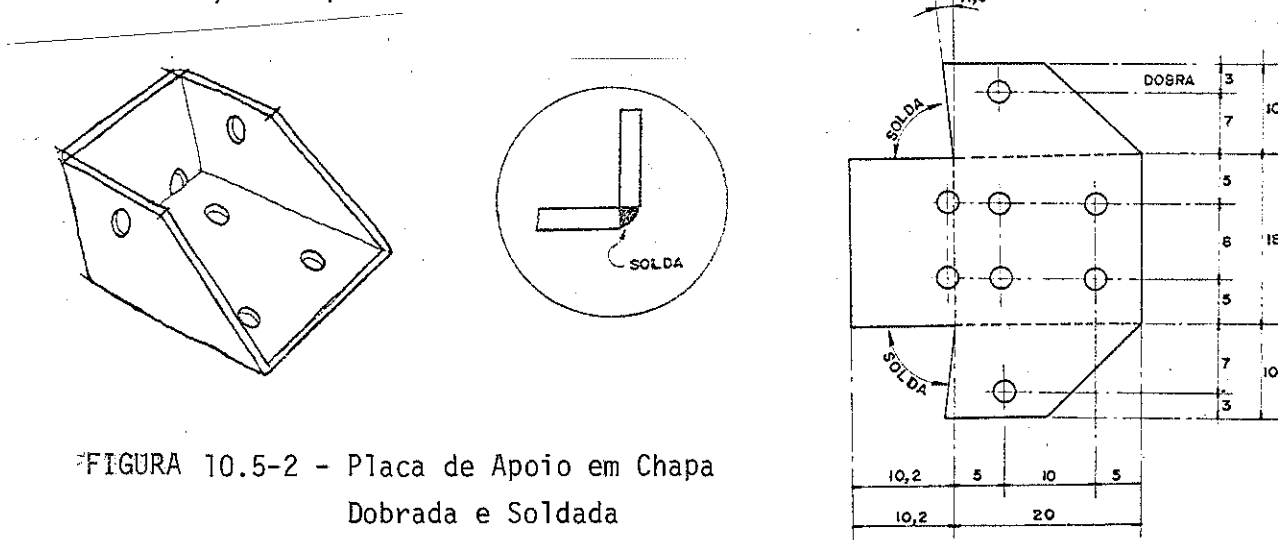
Placa de Apoio em Chapa Dobrada e Soldada
